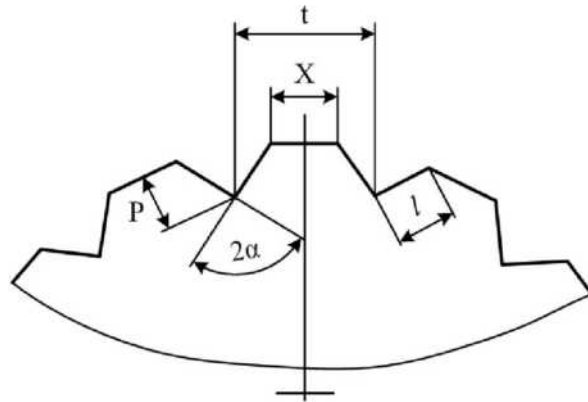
Профіль рифлень на бічній поверхні робочої частини пробивного пуансона
